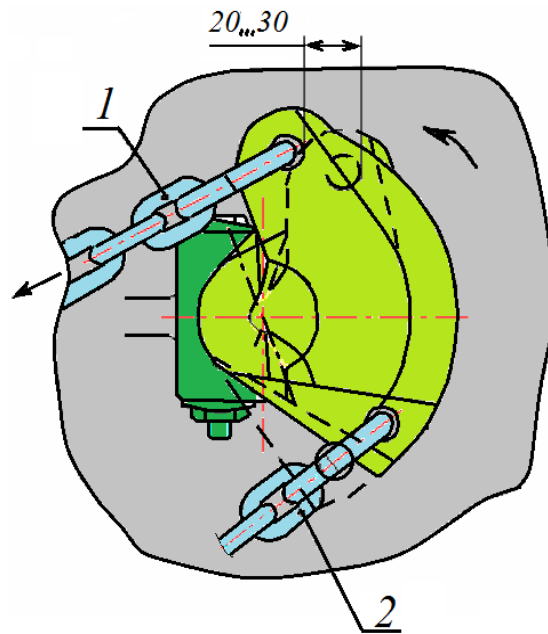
Положення валика підйомника під час перевірки роботи модернізованого розчіпного приводу
